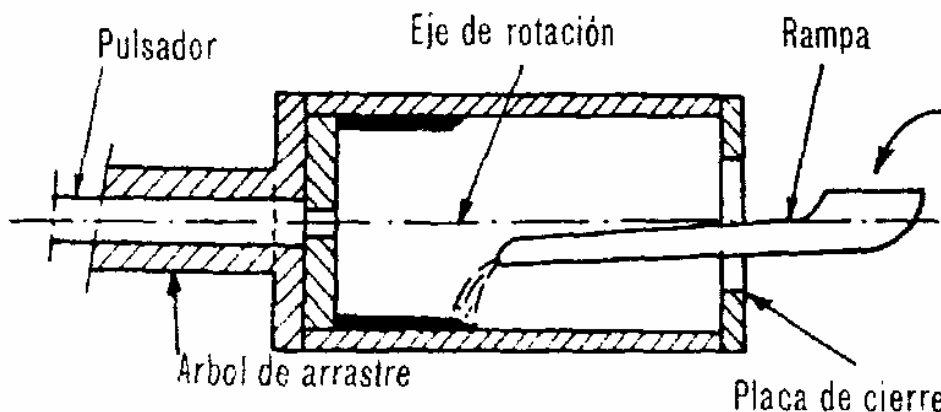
Moldeado en coquilla centrifugada sin macho.
